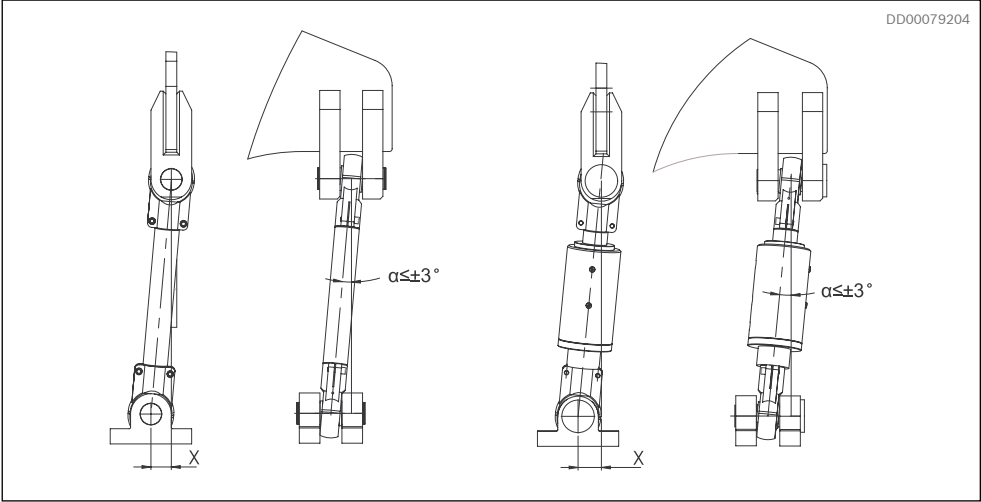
Instruções de instalação para a conexão articulada e o cilindro hidráulico para DTCBM 1600 a DTCBM 4000
